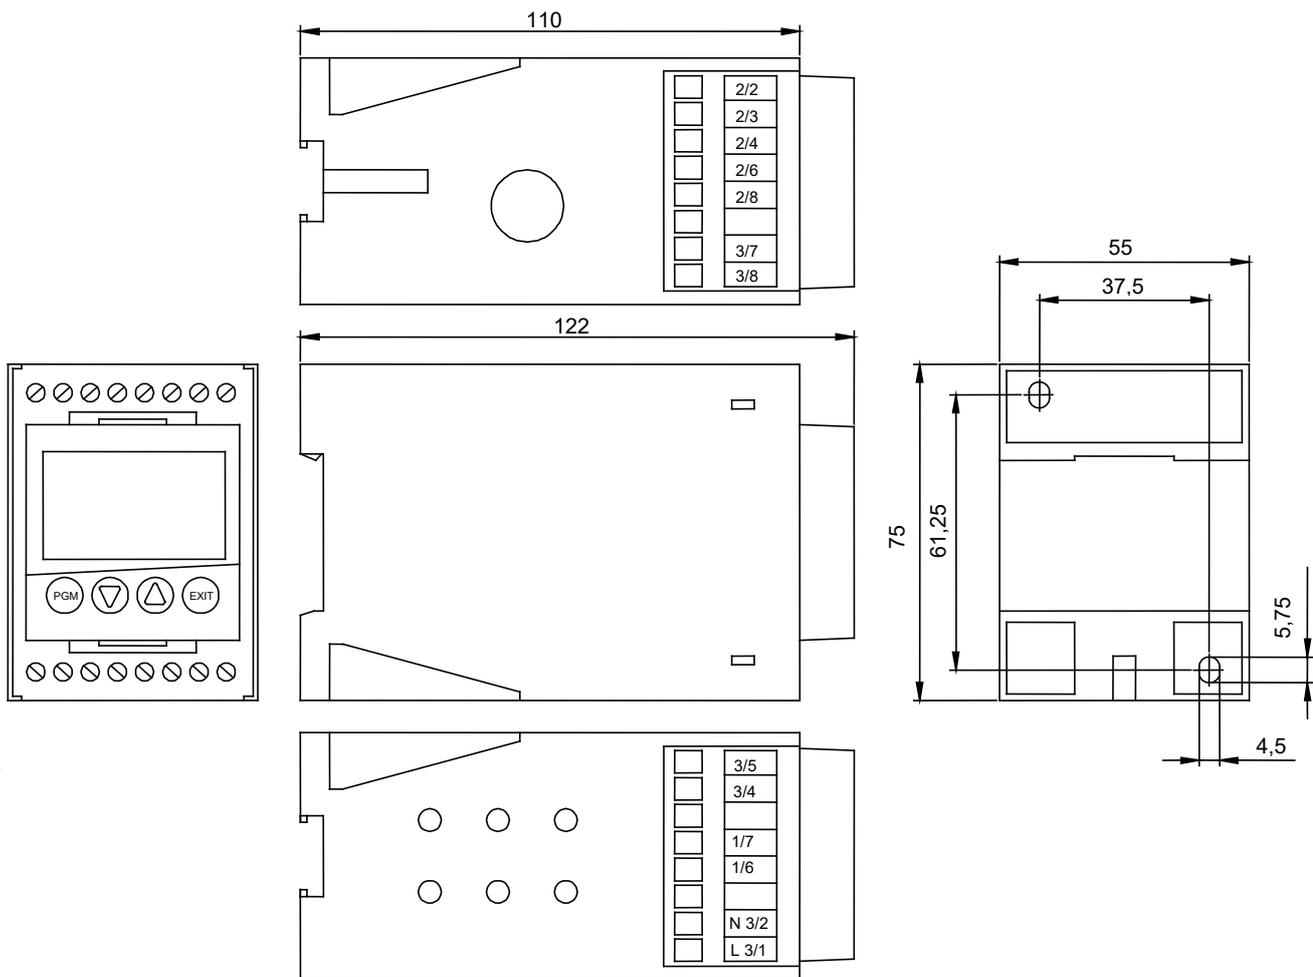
Gehäuseabmessungen und Montagemaße Regler 70304.2 für Schienenmontage
